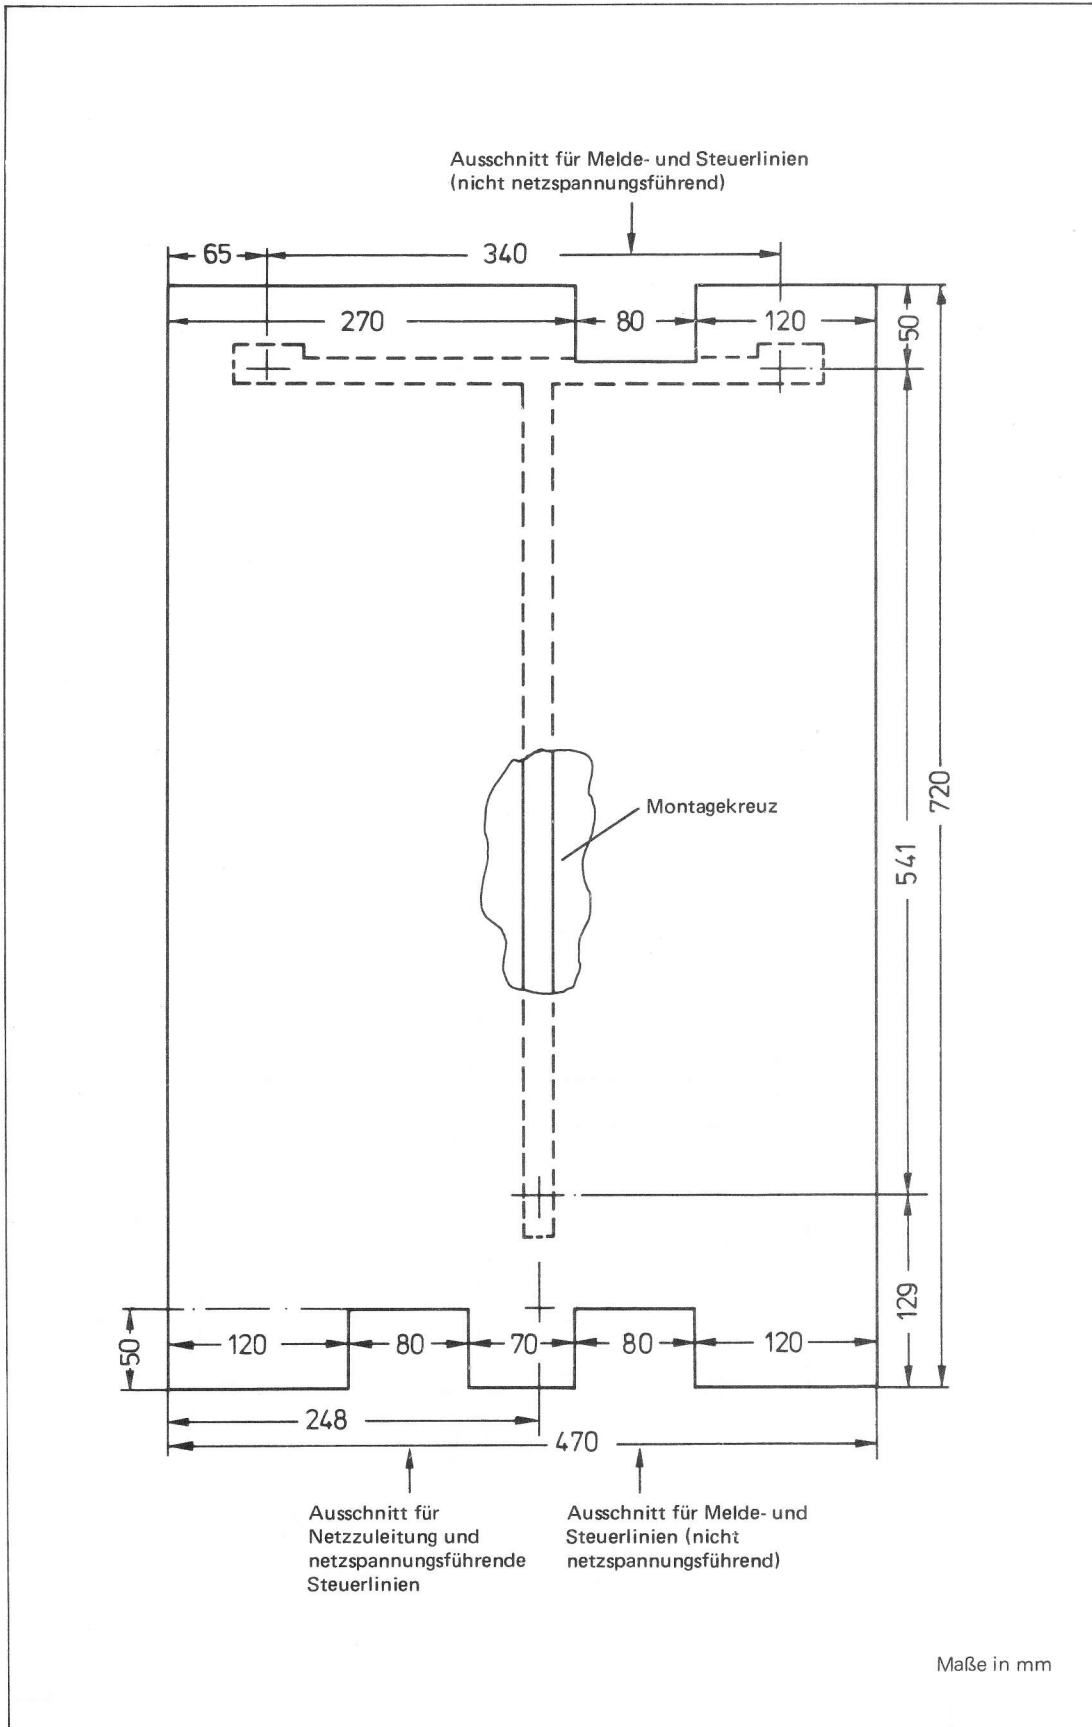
Abmessungen der Grundplatte sowie Lage der Ausschnitte für die Leitungseinführungen und Befestigungsmaße für das Montagekreuz
